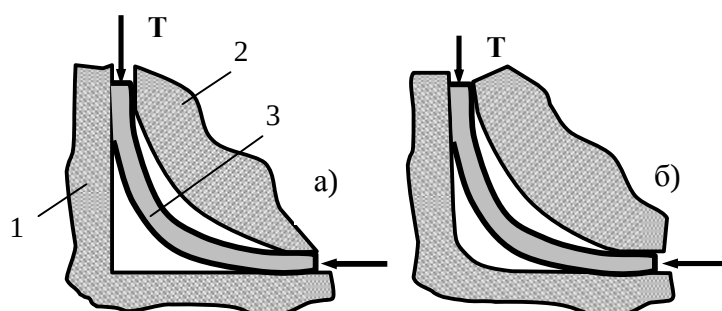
Формовки угловой зоны: 1 – охватывающий ролик; 2 – охватываемый ролик; 3 – заготовка; а – с двусторонним высвобождением; б – с высвобождением по внутреннему контуру и посадкой наружного контура;
